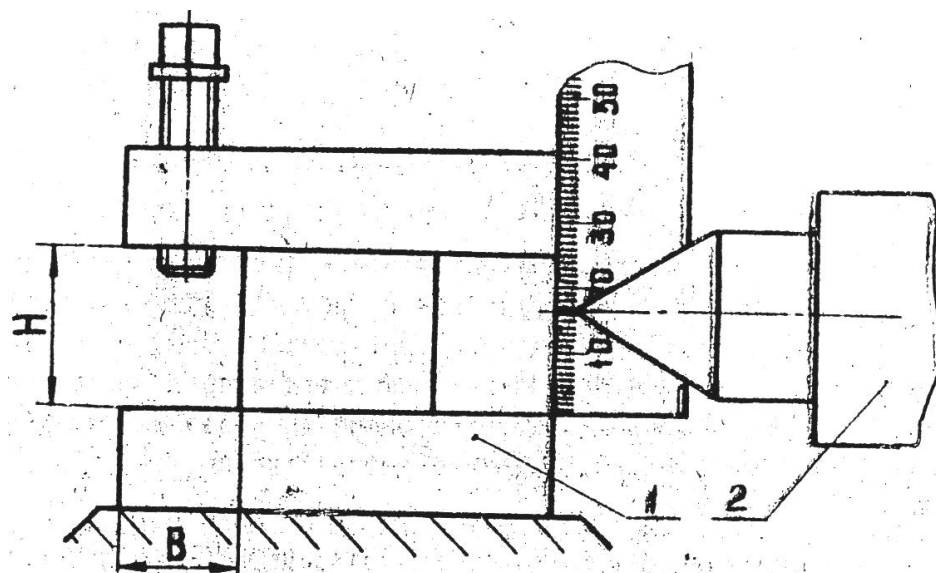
Схема измерения высоты от опорной поверхности резца до линии центров: 1 – резцедержатель; 2 – пиноль.
